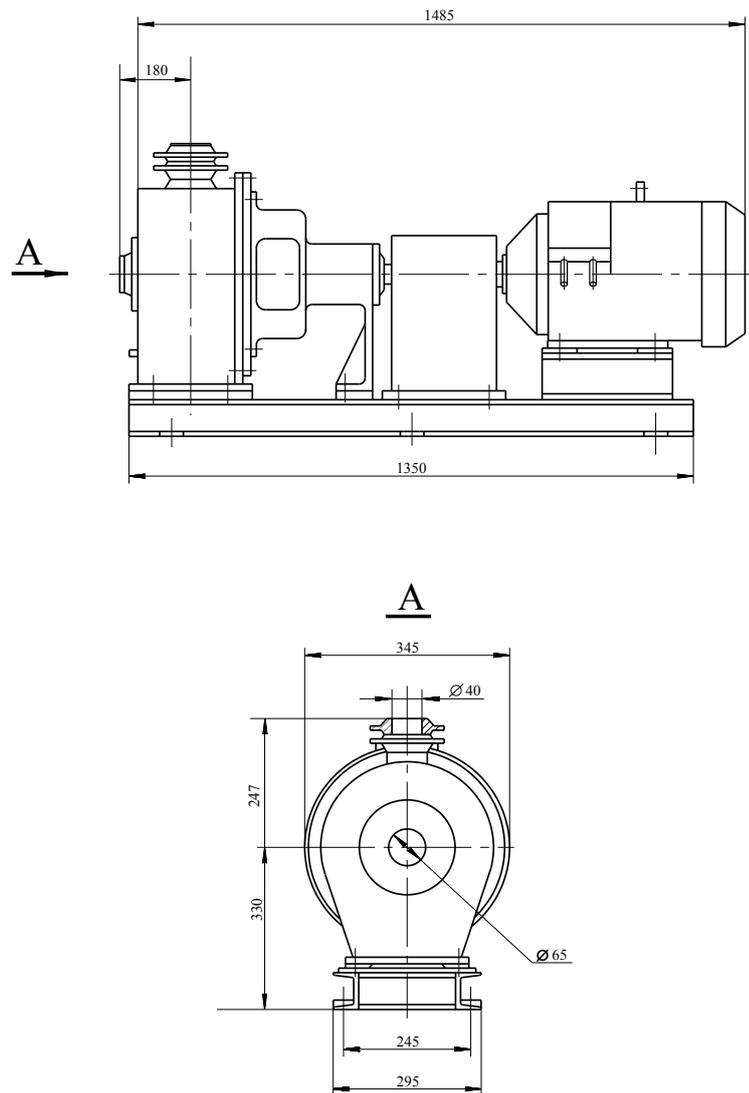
Габаритный чертеж насоса бака боросодержащих дренажей
